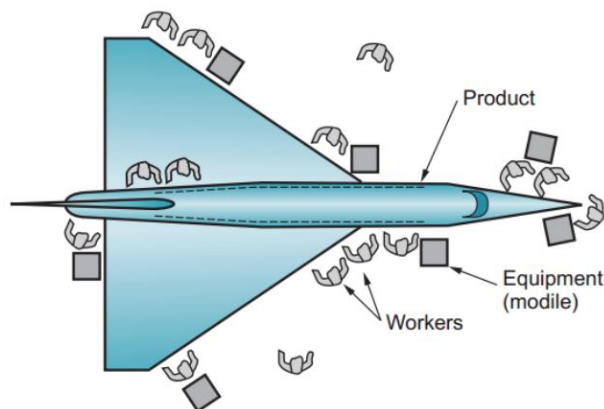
Exemplo de um *layout* de posição fixa aplicado na construção de aviões (Molla, 2018).
